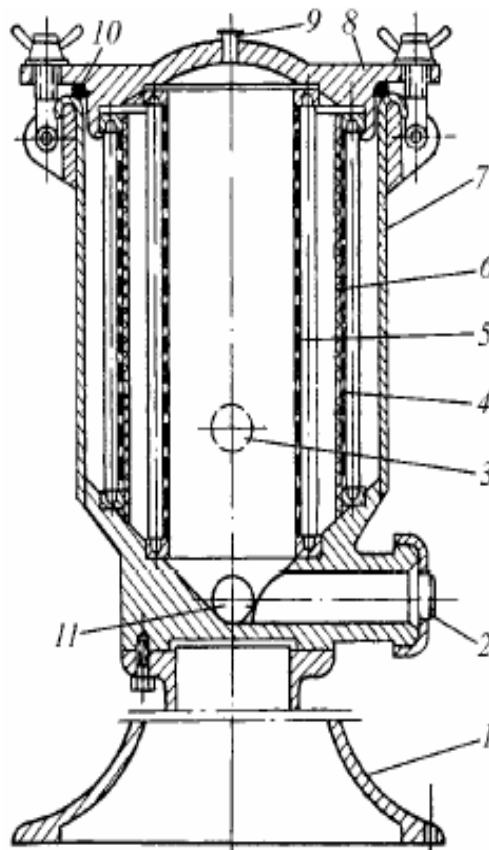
Закрытый цилиндрический фильтр для молока
